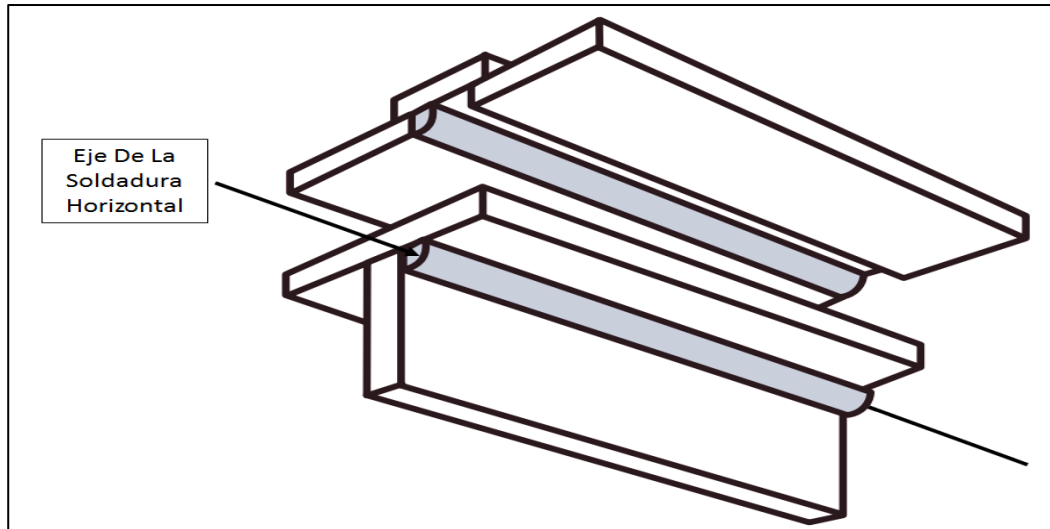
Soldadura De Filete En Posición 4F [58].
